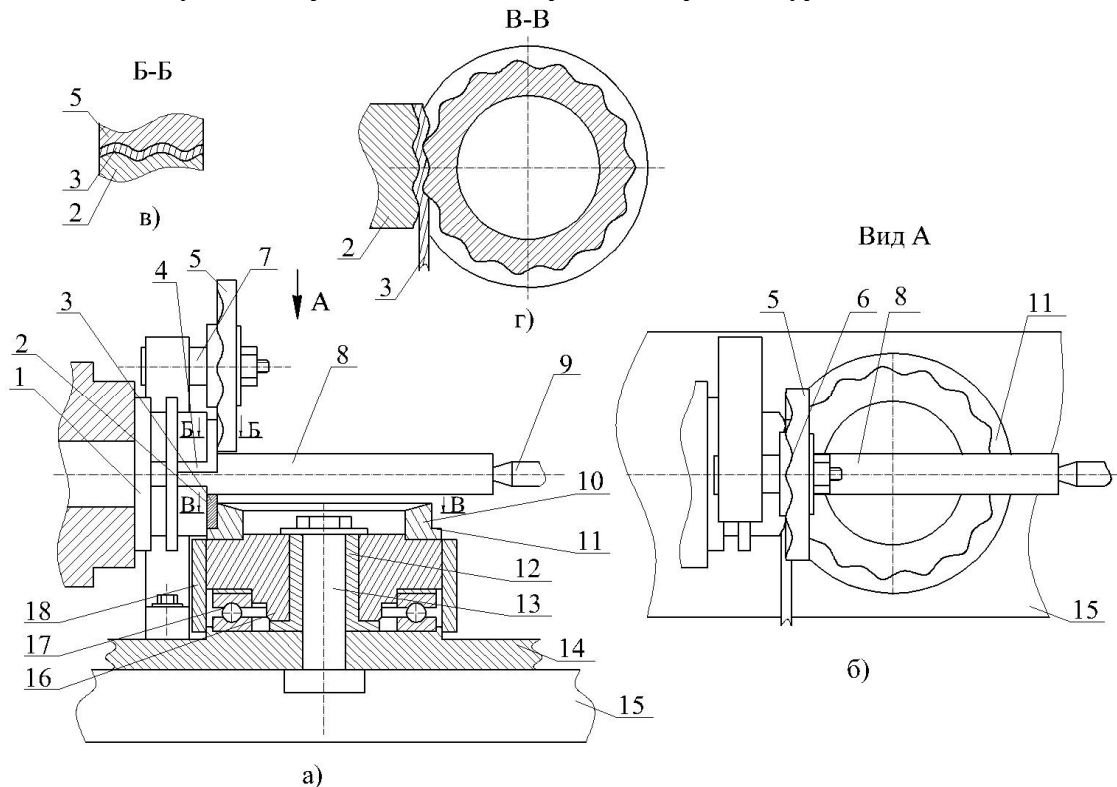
Пристрій для виготовлення гвинтових гофрованих заготовок:
